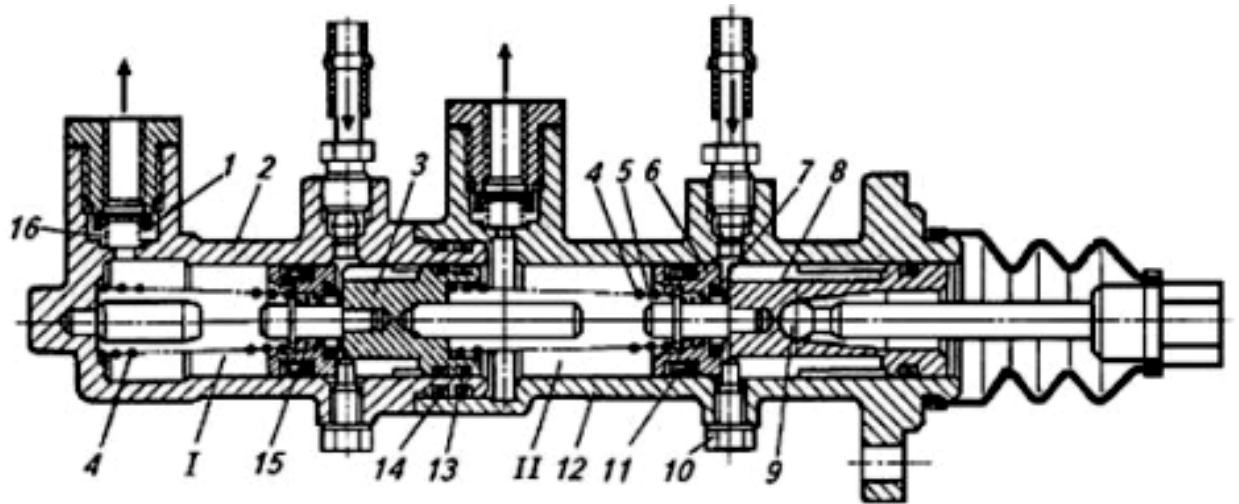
Главный тормозной цилиндр автомобиля ГАЗ: I, II - полости главного тормозного цилиндра; 1 - клапан избыточного давления; 2, 12 - соответственно вторичный и первичный картеры; 3, 8 - соответственно вторичный и первичный поршни; 4 - возвратные пружины поршня; 5 - упорный стержень; 6 - головка поршня; 7 уплотнительное торцевое кольцо; 9 - толкатель; 10 - упорный болт; 11 - манжета; 13, 14 - соответственно уплотнительные кольца поршня и корпуса; 15 - пружина головки поршня; 16 - пружина клапана избыточного давления
